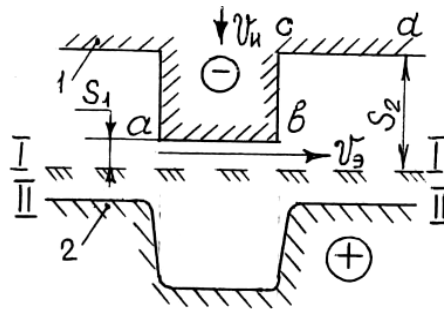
Схема отримання заглиблення при ЕХО: 1 – електрод-інструмент; 2 – заготовка
